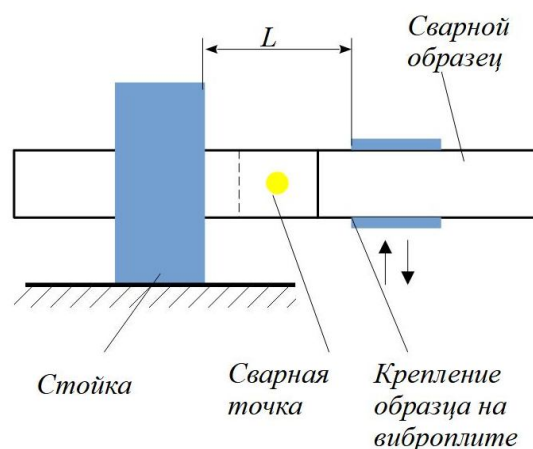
Схема испытаний вибрационной прочности сварных образцов
